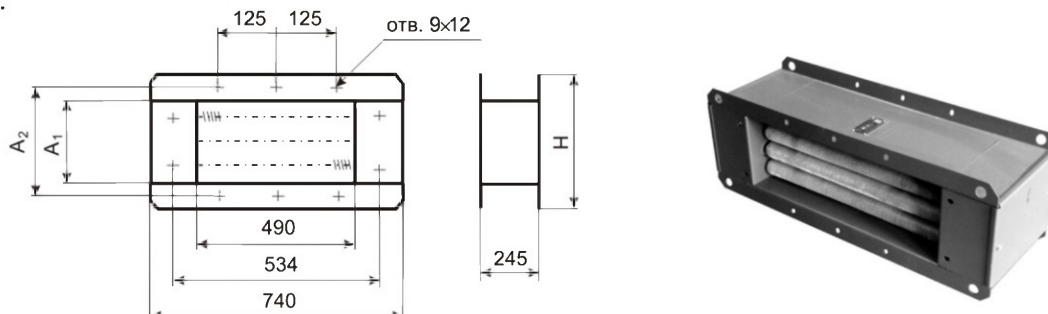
Габаритно-присоединительные размеры ВЭ
